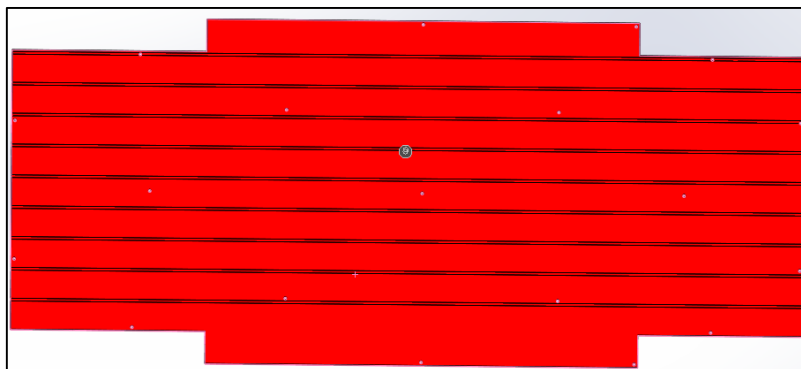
Fondo plano. Fuente: CAD fondo plano
